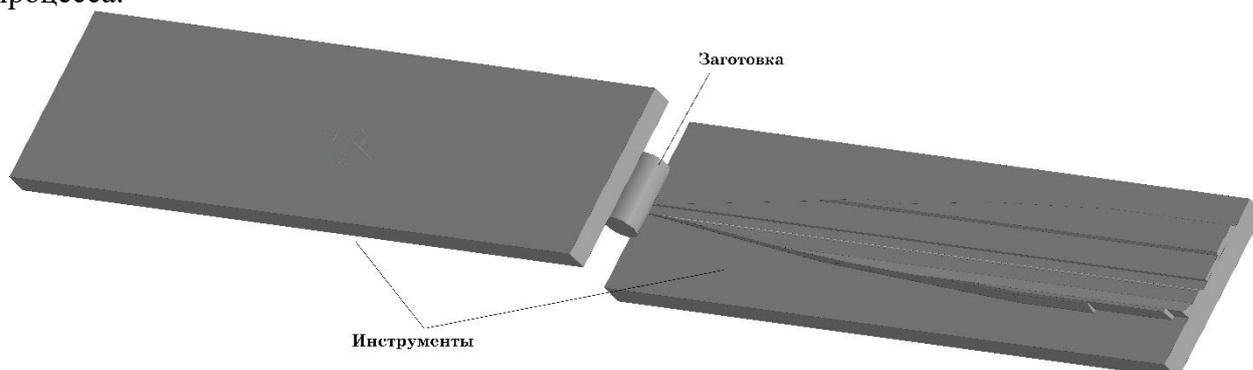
Схема процесса поперечно клиновой прокатки для получения поковки резца «РШ 38/30-75L53/19».
